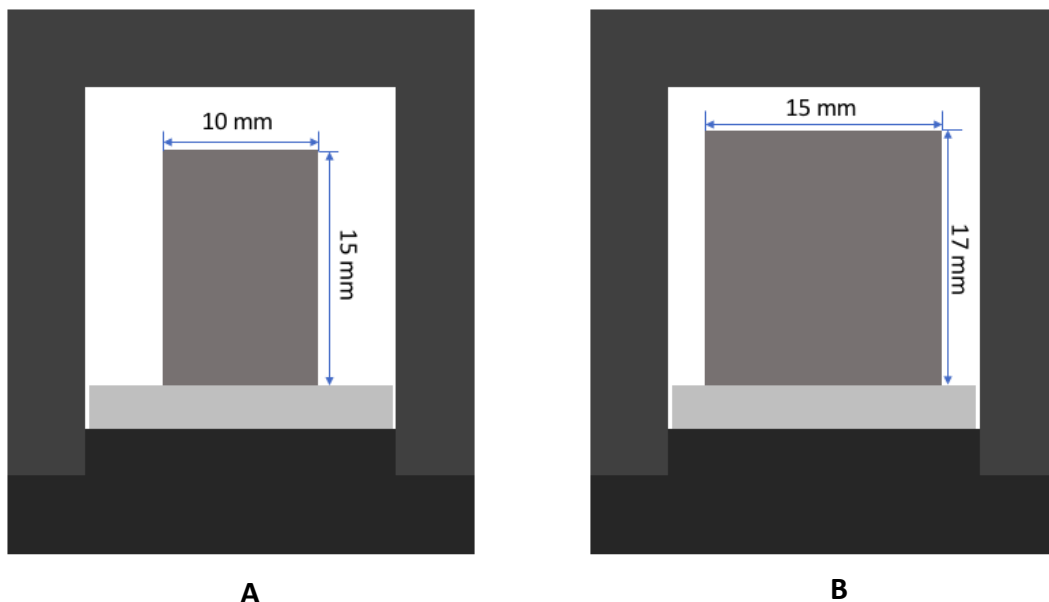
Dimensiones originales de la probeta de acero (a) y dimensiones de la probeta de acero de tamaño aumentado (b).
